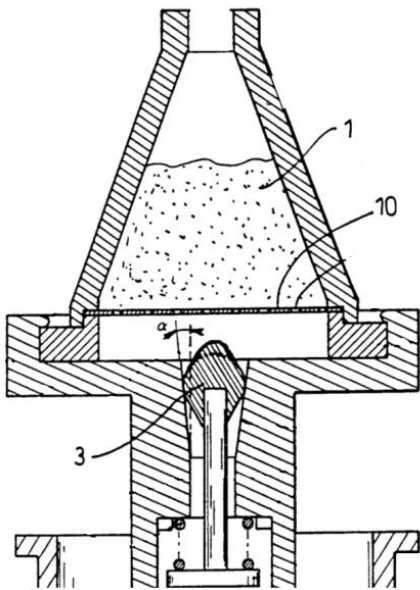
Stab (3) schlägt auf eine flexible Membran (10) und löst so Vibrationen im Pulverbett (1) aus.⁽⁷¹⁾
